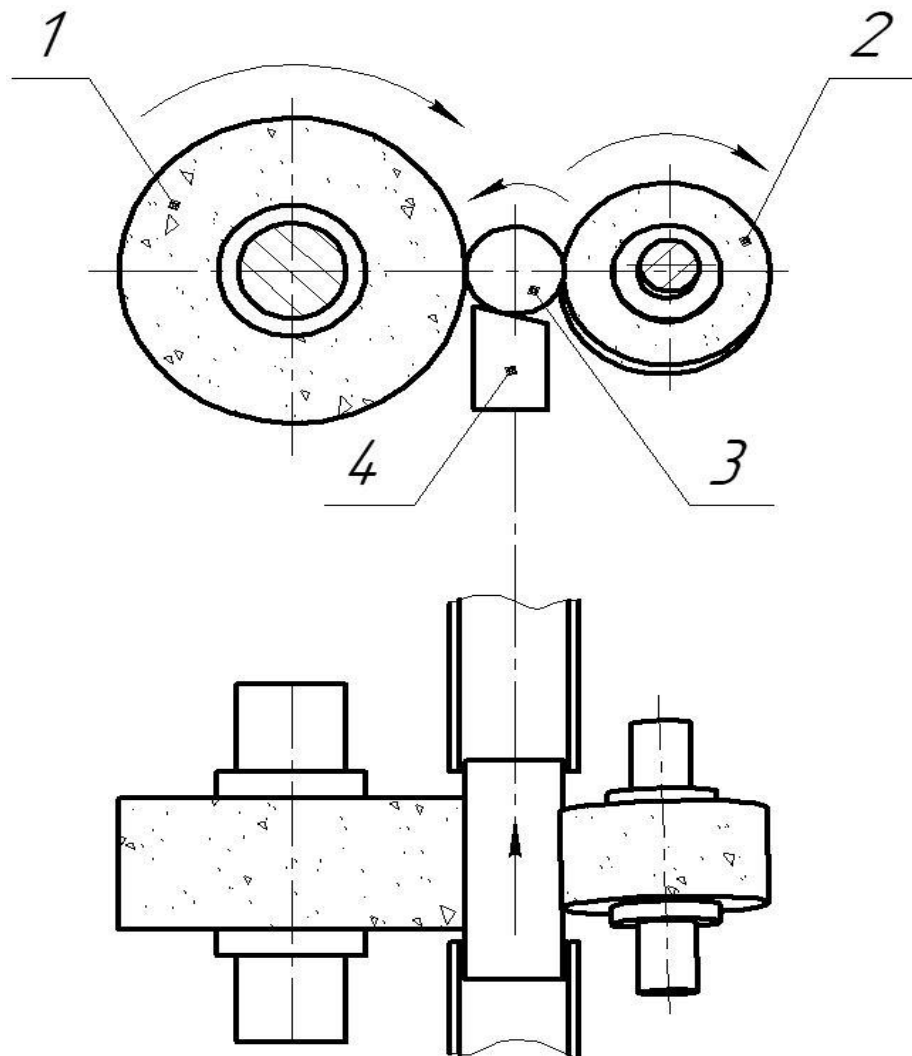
Схема безцентрового шліфування: 1 – робочий круг; 2 – приводний круг; 3 – заготовка; 4 – ніж для підтримки заготовки
